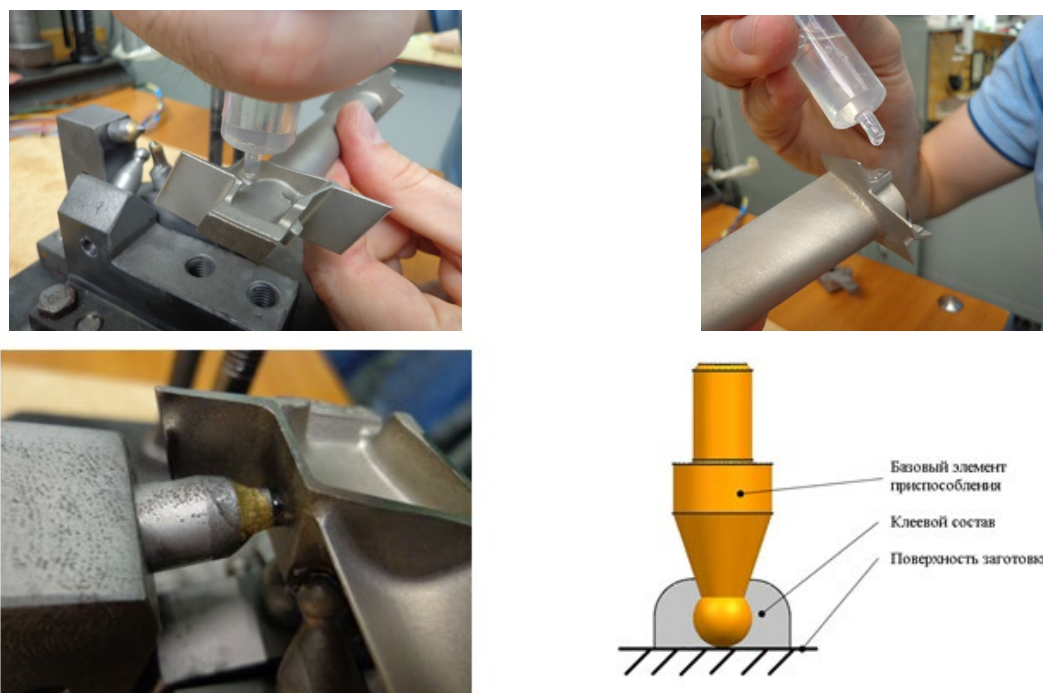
Закрепление детали типа лопатка турбины методом приклейки
